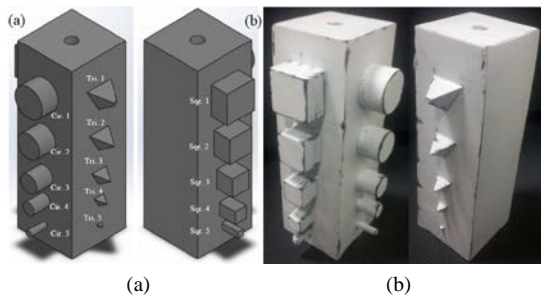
Prueba de figuras geométricas (a) Diseño CAD y (b) pieza impresa.
